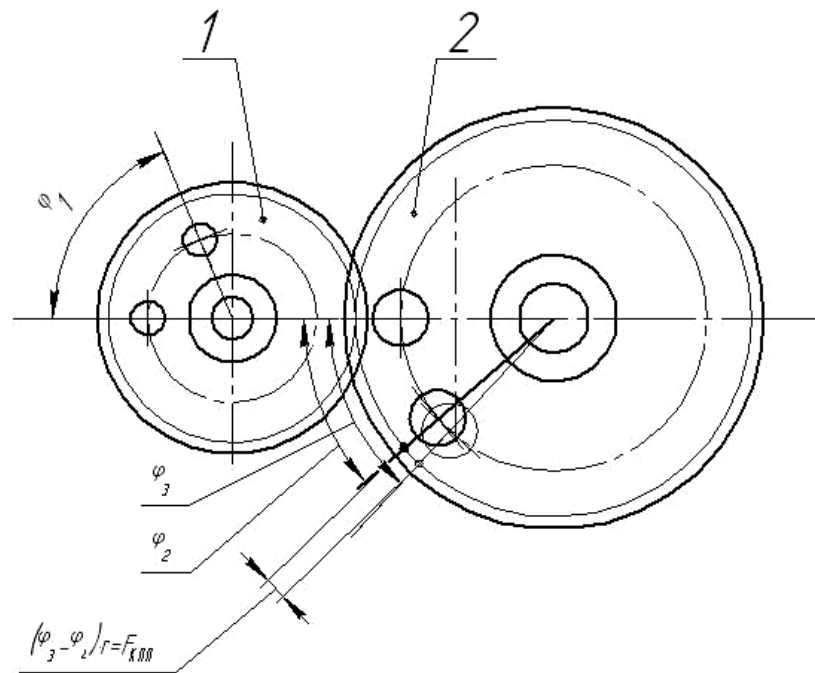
Схема зубчатой передачи к определению ее кинематической точности
